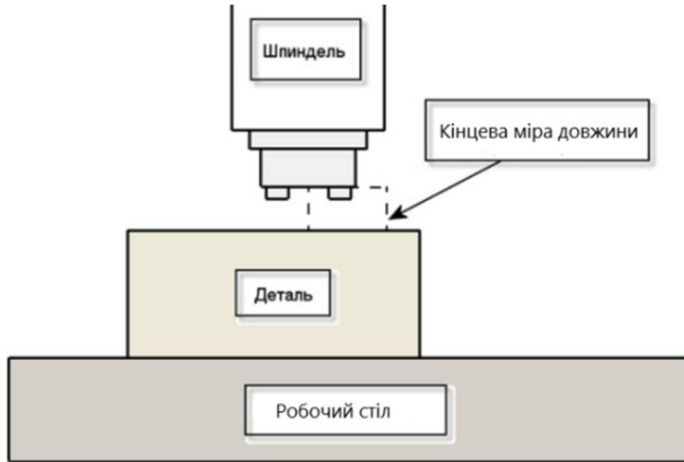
Установка нульової точки заготовки по осі Z за допомогою кінцевих мір довжини
